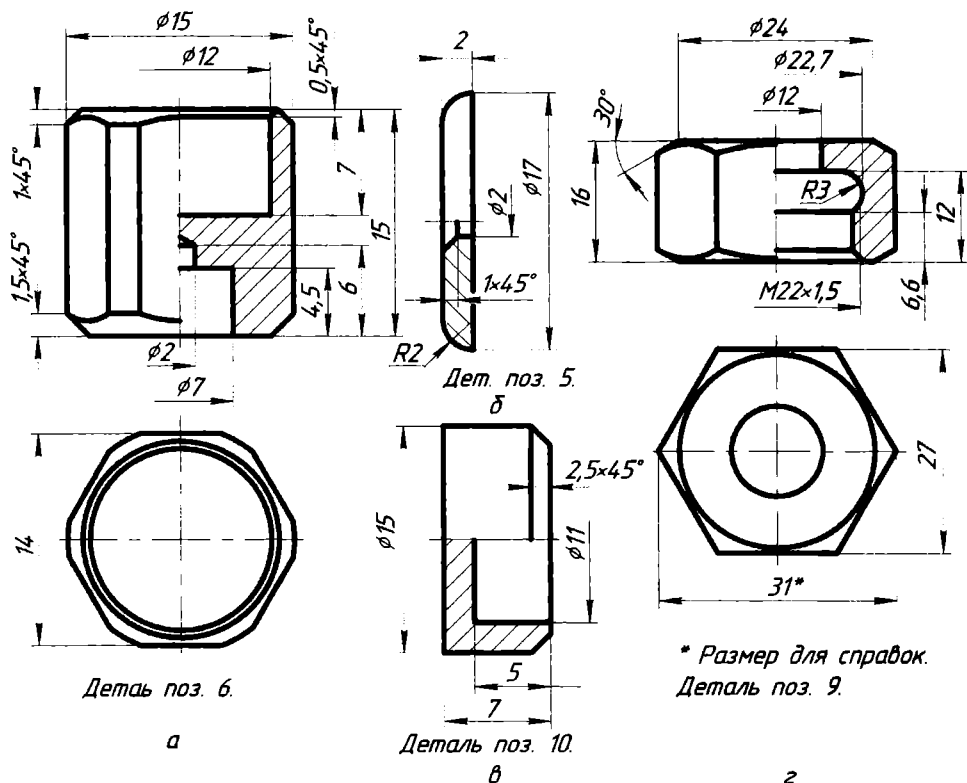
Чертежи: а — седла; б — втулки; в — стержня
